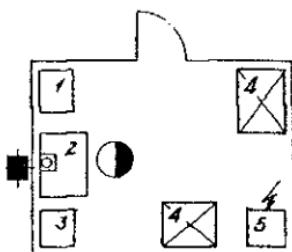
Планировка поста электродуговой сварки:
